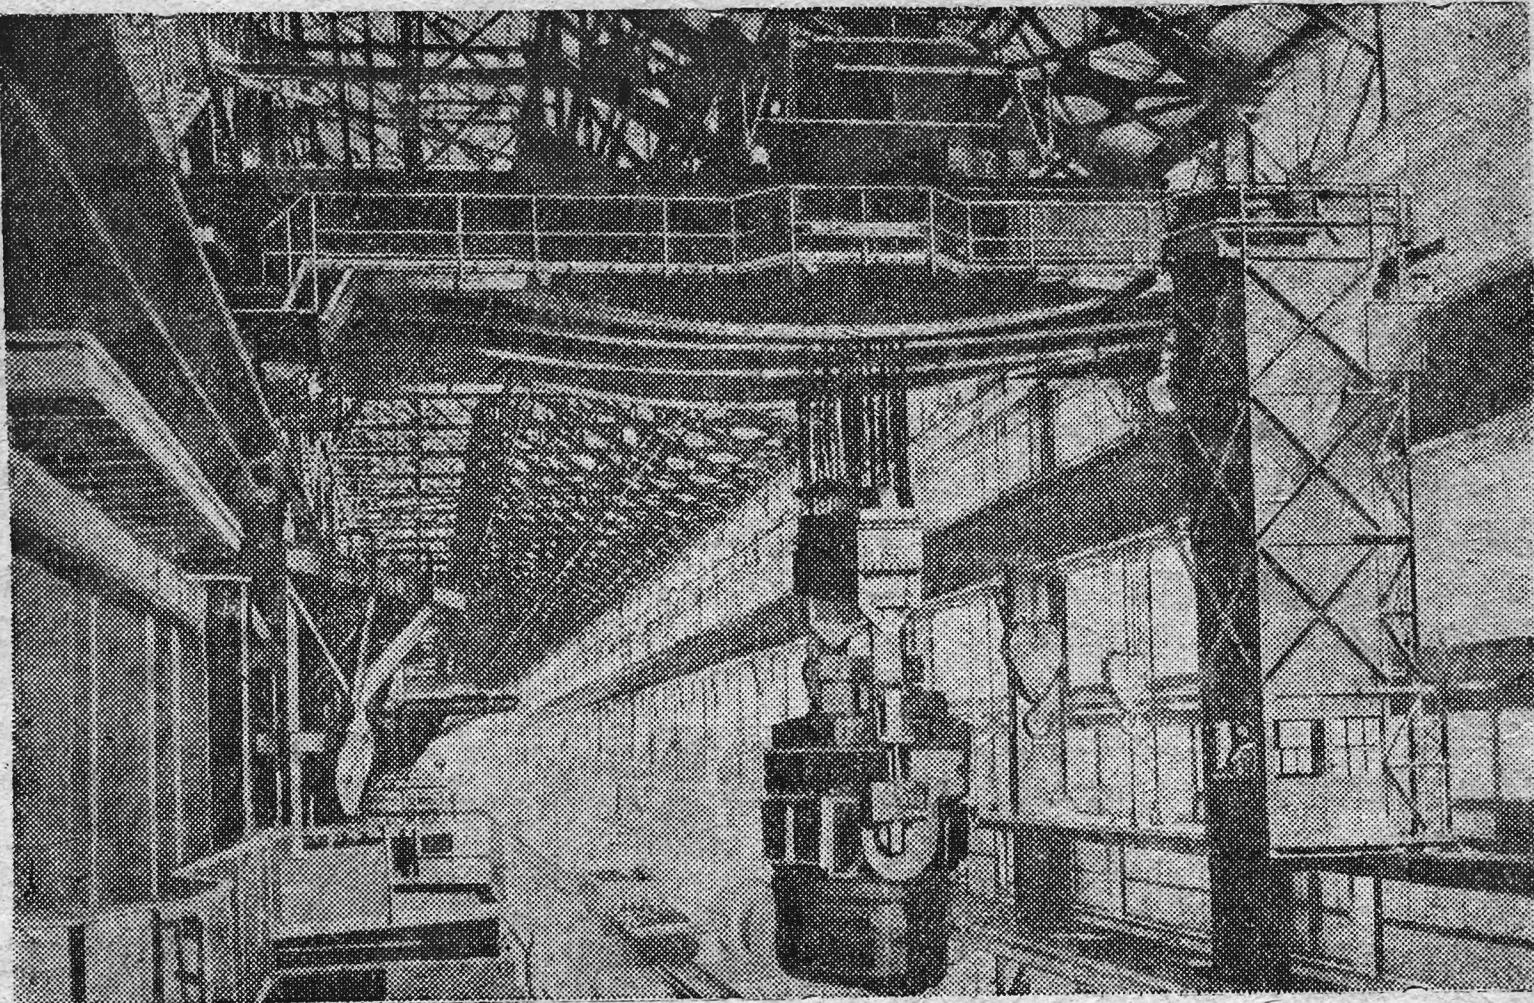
Разливочный пролет главного здания мартеновского цеха с 15 печами. На переднем плане видно испытание ковша и крапа на пробную нагрузку в 200 тонн.
